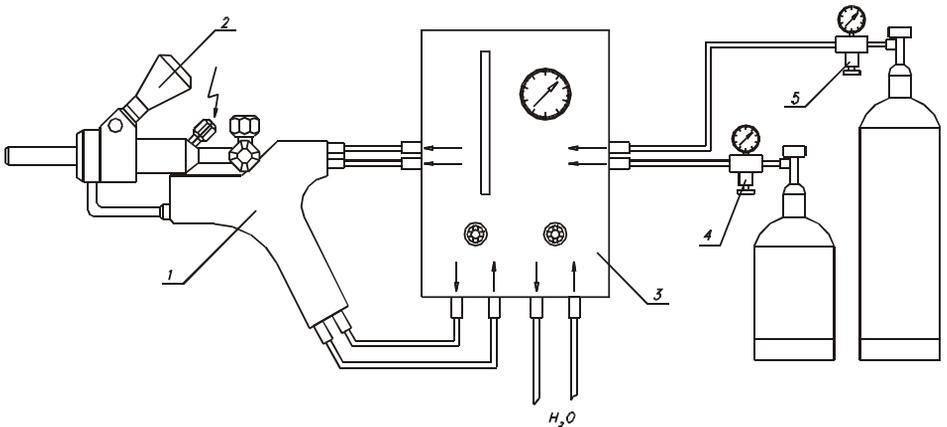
Схема сверхзвуковой газовой горелки установки СГН-1:
